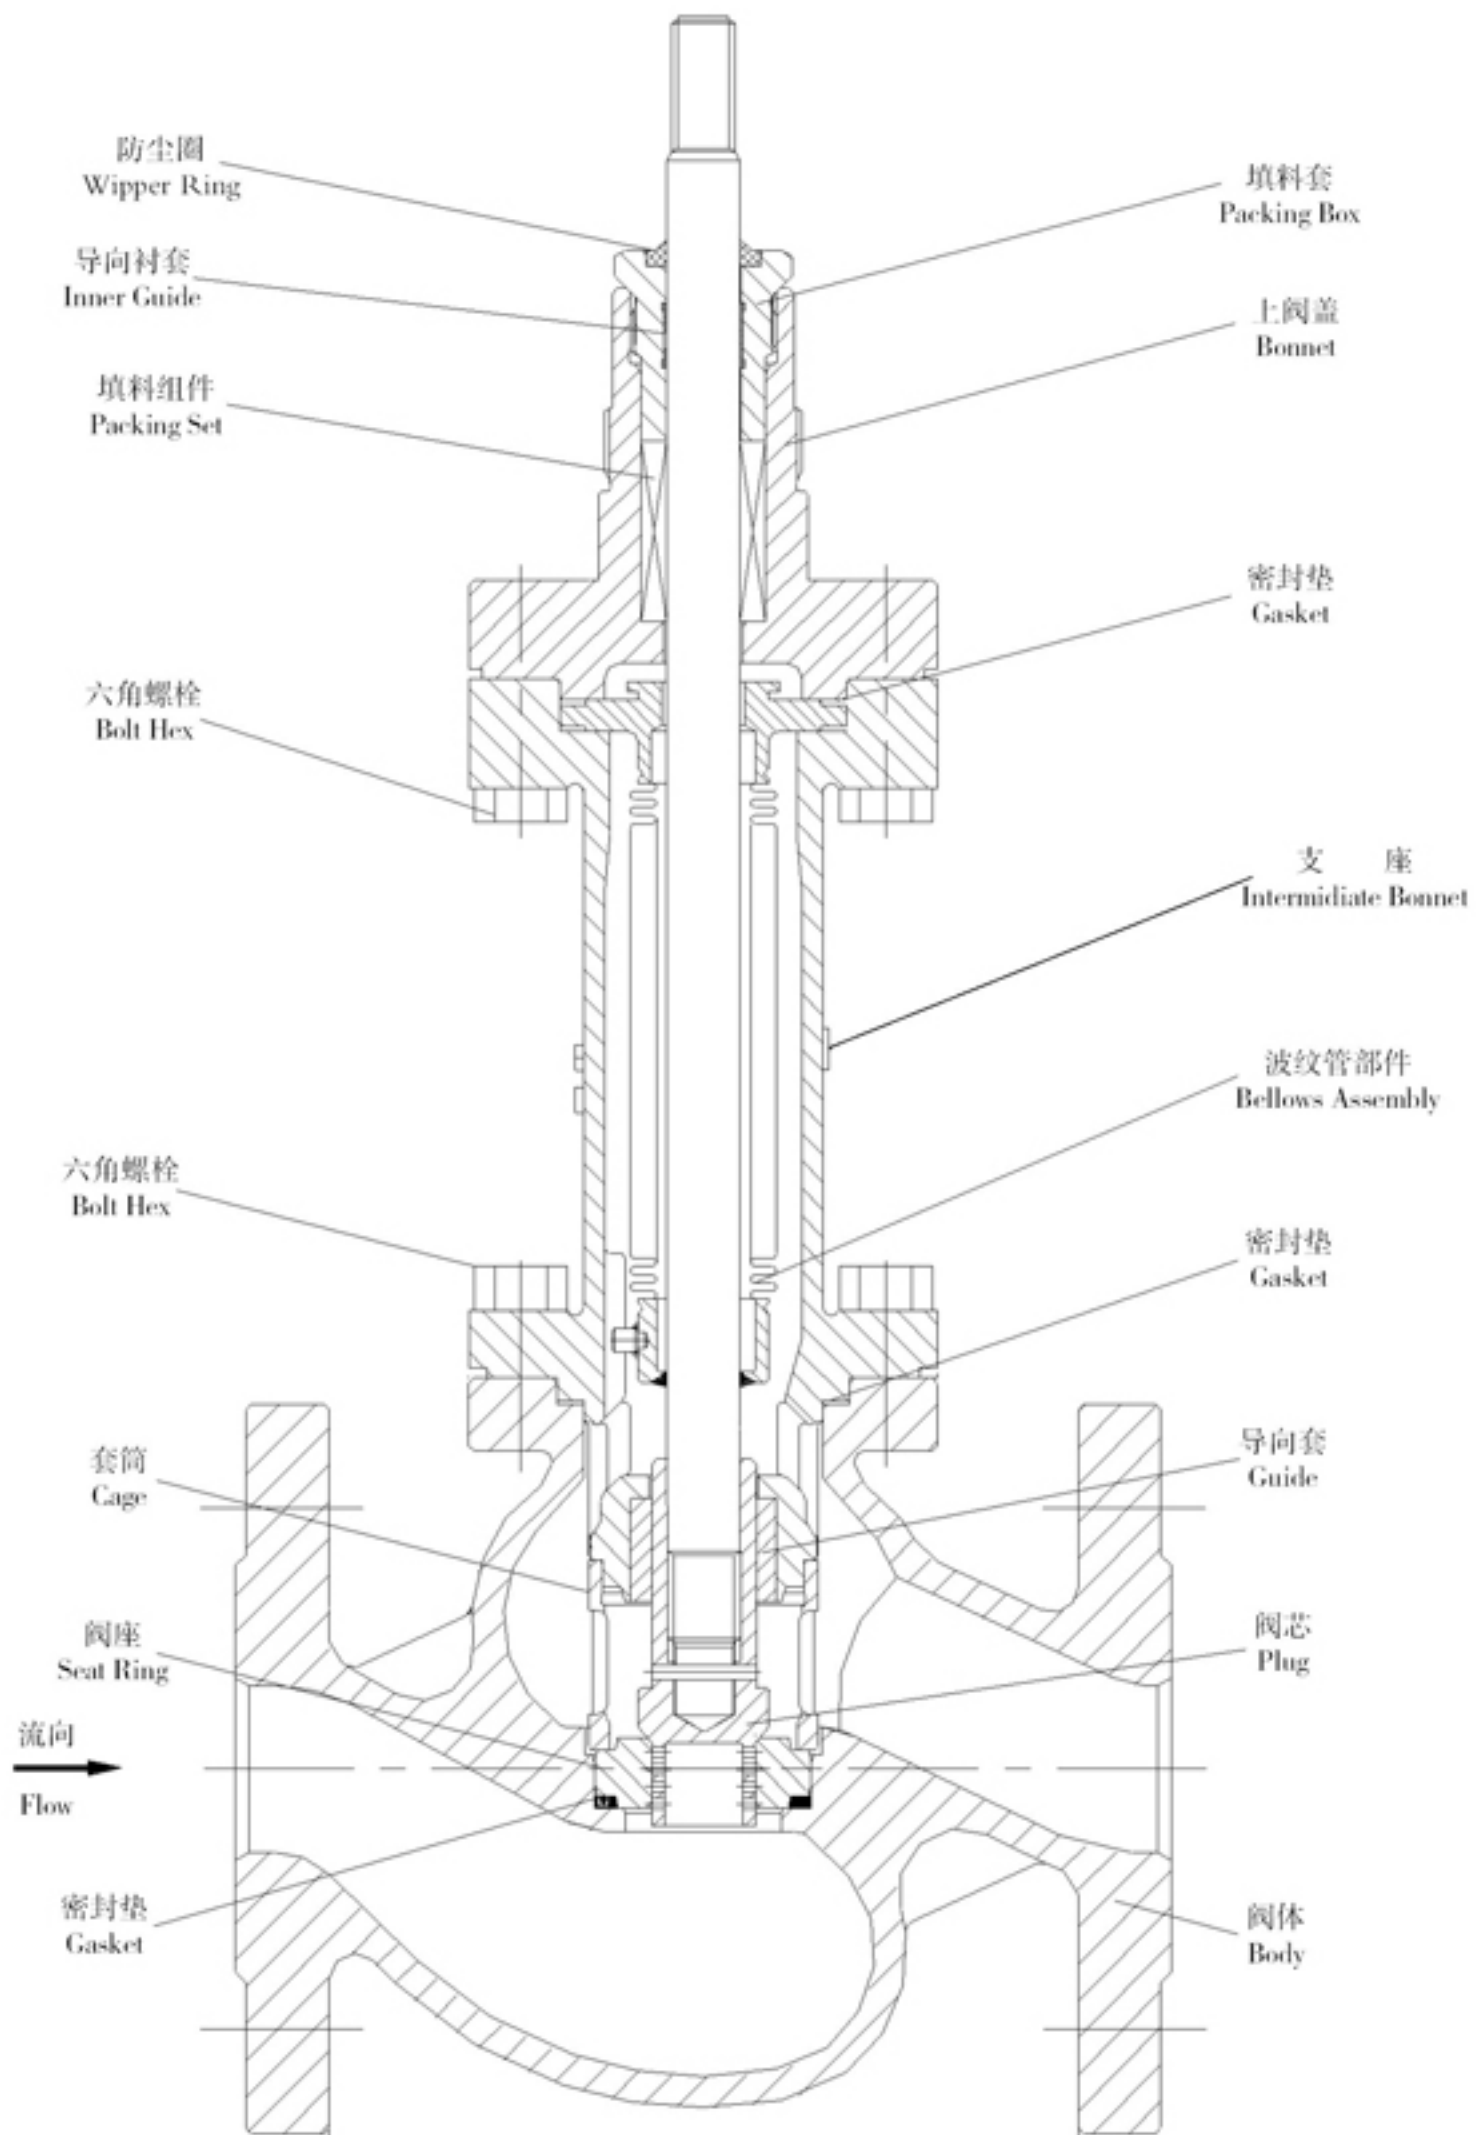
本体部构造 Fig.3 BODY SECTION VIEW
